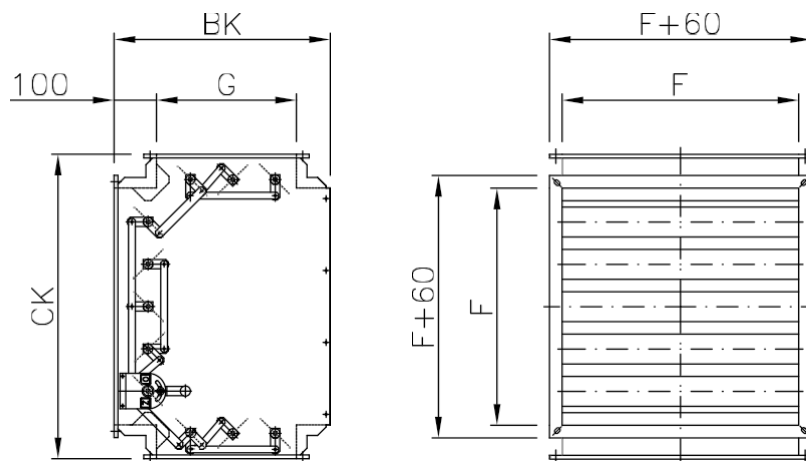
Mischkammer, Ausführung ohne Filtergewebe mit manueller Steuerung
